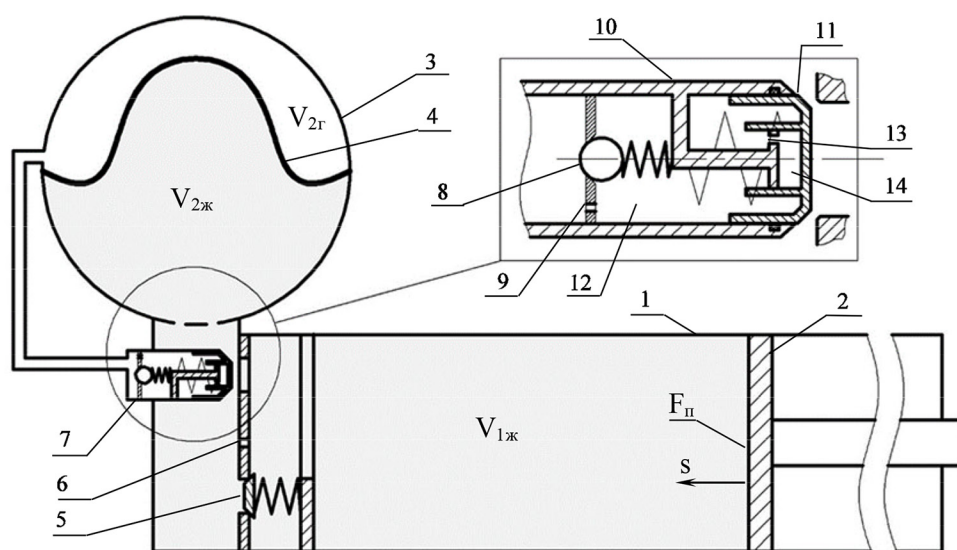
Схема ПГА: 1 – РК; 2 – шток с поршнем; 3 – ОАД; 4 – разделительная мембрана ОАД; 5 – обратный клапан ОАД; 6 – дроссель ОАД; 7 – напорный клапан; 8 – обратный клапан напорного клапана; 9 – дроссель малого сечения; 10 – неподвижный корпус напорного клапана; 11 – подвижная тарель напорного клапана; 12 – газовая полость; 13 – дроссель демпферной полости; 14 – демпферная полость
